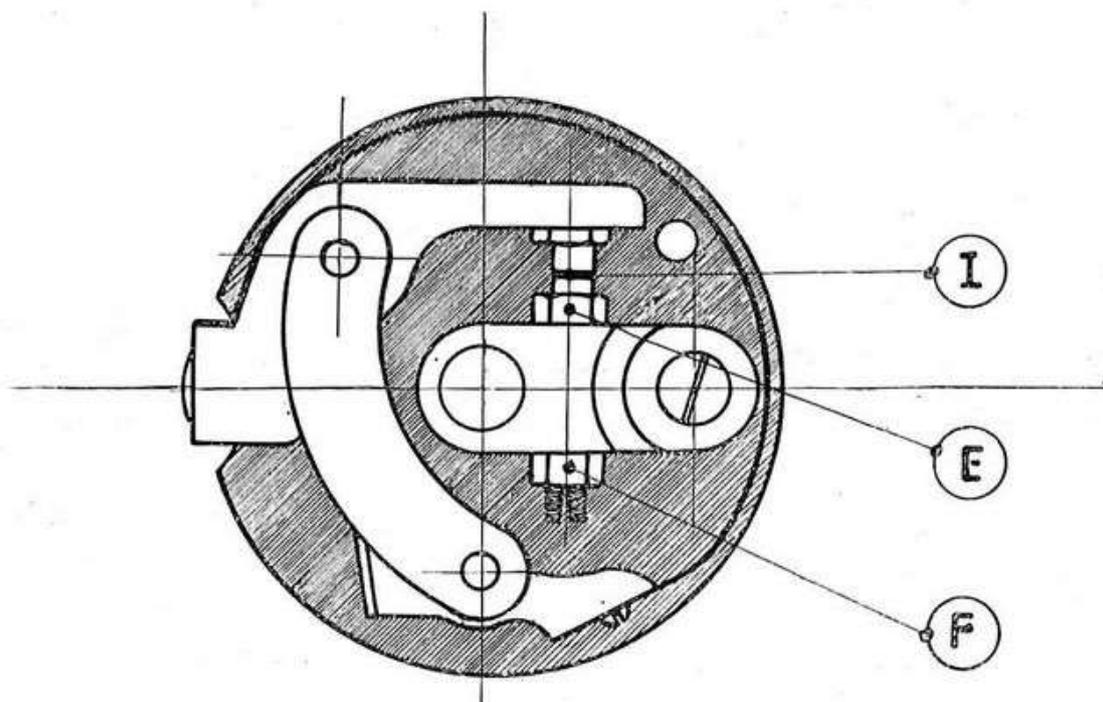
Rullatore per Magnete e Dinamo Magnete.
